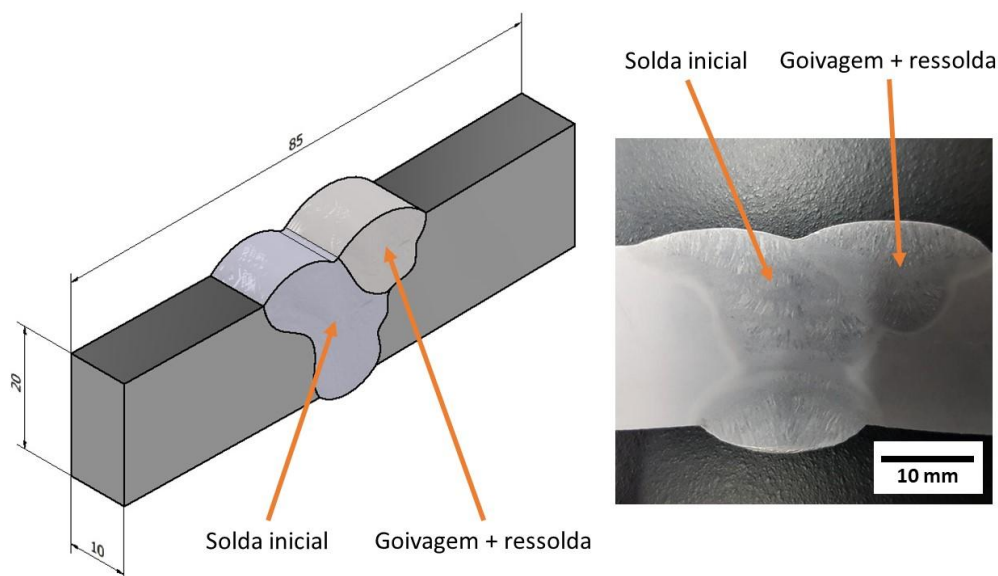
Representação das amostras cortadas, (a) dimensões das amostras utilizada com indicação da região solda e ressoldada (goivada), (b) macrografia com ataque Vilella indicando a região com solda inicial e região goivada e ressoldada.
